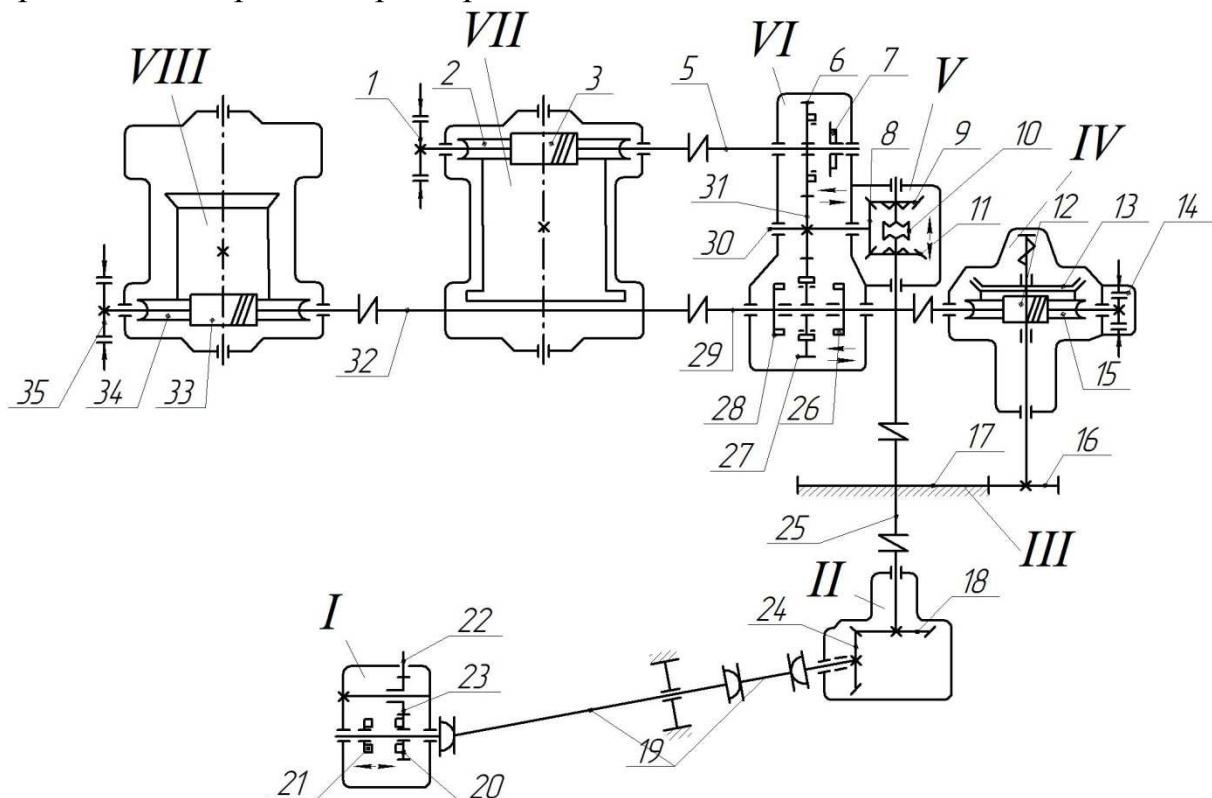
Кинематическая схема крана КС-2561Д: I – коробка отбора мощности, II – нижний конический редуктор, III – опорно-поворотное устройство, IV – механизм поворота, V – реверсивный механизм, VI – распределительная коробка, VII, VIII – грузовая и стреловая лебедки
